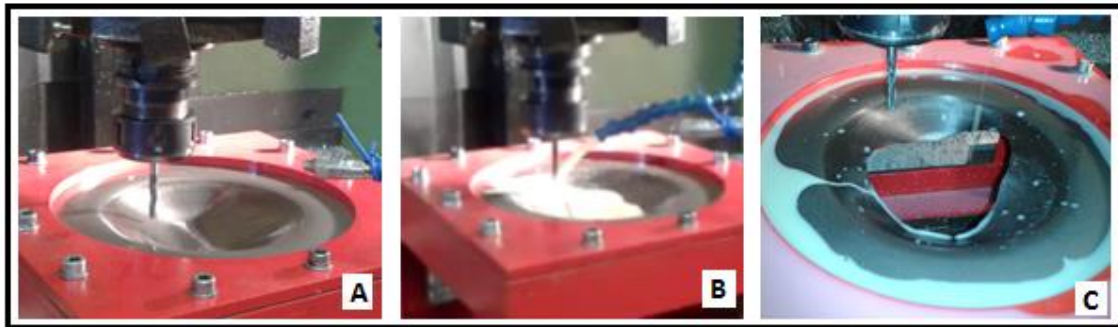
Etapas de Corte em ISF (A) Posicionamento da Fresa (B) Introdução do líquido de arrefecimento (C) corte final.
